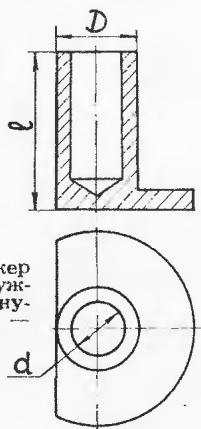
Новый плунжер из заклепки: D — наружный диаметр; d — внутренний диаметр; 1 — длина.
